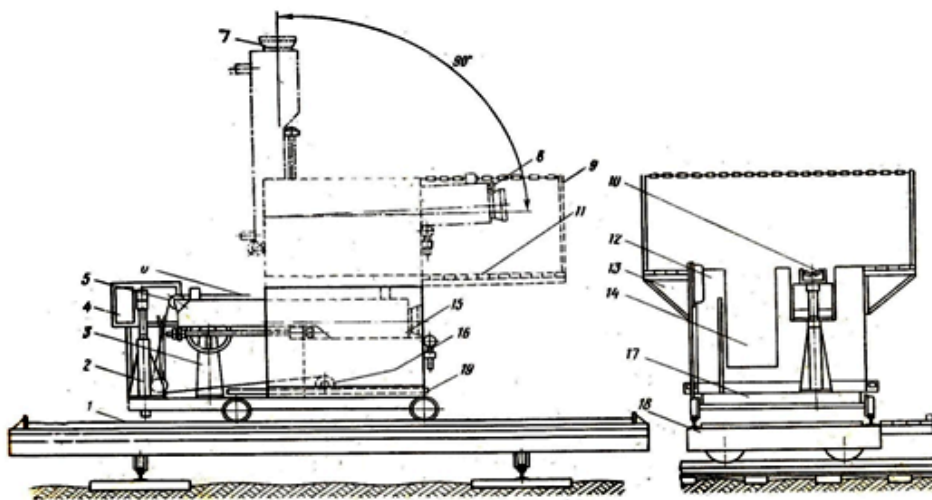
Агрегат сліповий монтажний типу АСМ-1
